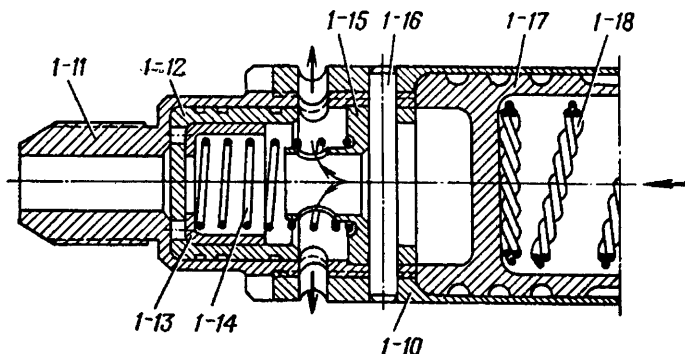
Положение деталей агрегата пневмозарядки (обозначения деталей см. в приложении 1)
